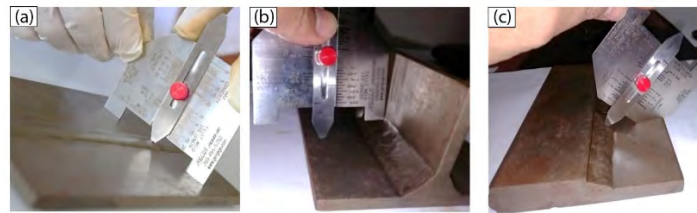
Disposición de Weld Size Gauge para dimensionar el tamaño de (a) refuerzo en junta a tope (b) pierna en junta en T y (c) garganta en junta de solape
